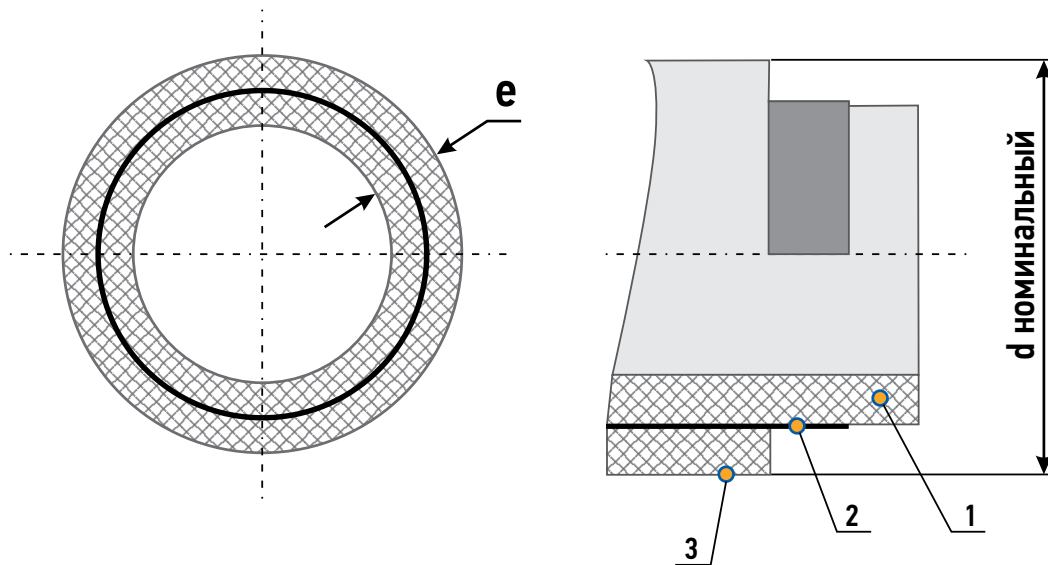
Схема трубы типа армирования внутри стенки трубы
